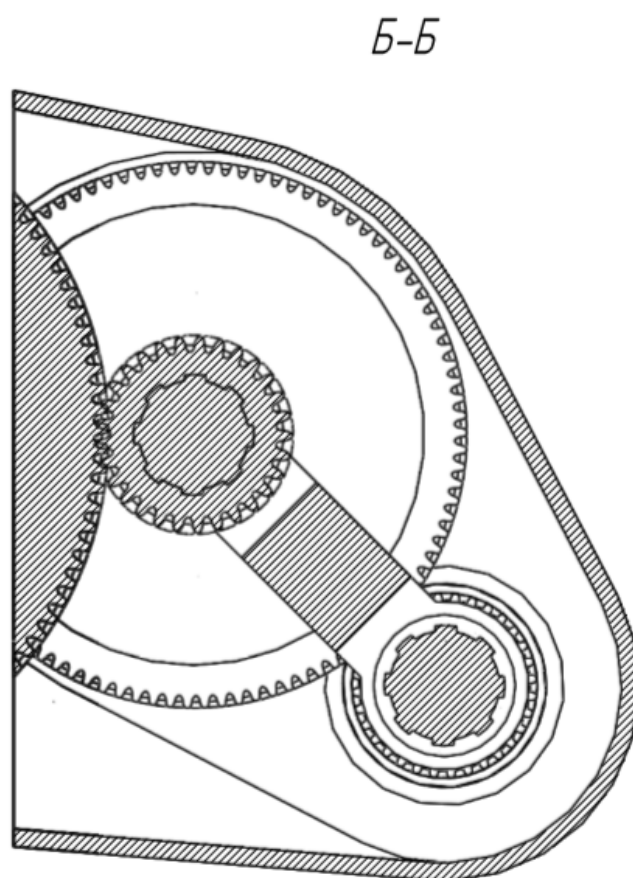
Загальний вигляд заднього редуктора(Розріз Б-Б).
